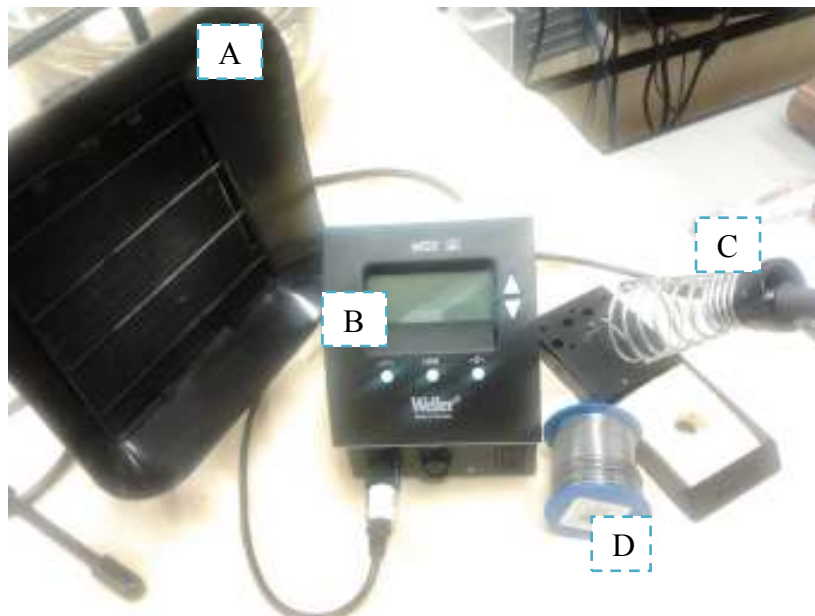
Equipamento de solda. (A) Filtro de ar, (B) Medidor e controlador de temperatura da solda do fabricante Weller (Estação de solda), (C) ponteira de solda em um suporte para solda, (D) rolo de fio de Pb/Sn (60/40%) usado para solda.
